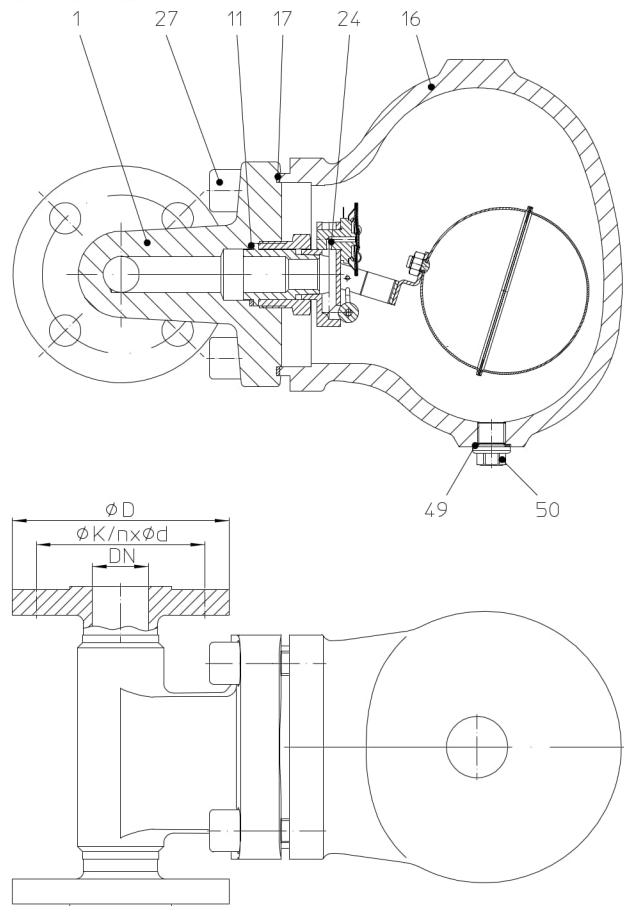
1 mit Flanschen - horizontale Einbaulage
